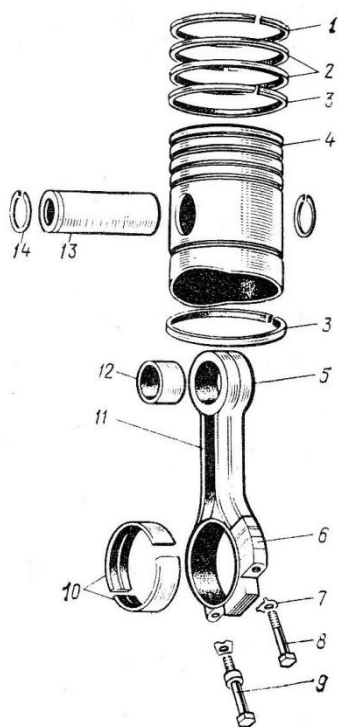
Шатунно-поршневая группа: 1,2 – компрессионные кольца; 3 – маслосъемные кольца; 4 – поршень; 5 – верхняя головка шатуна; 6 – крышка нижней головки шатуна; 7 – стопорная шайба; 8,9 – шатунные болты; 10 – вкладыши; 11 – стержень шатуна; 12 – втулка; 13 – палец; 14 – стопорное кольцо
